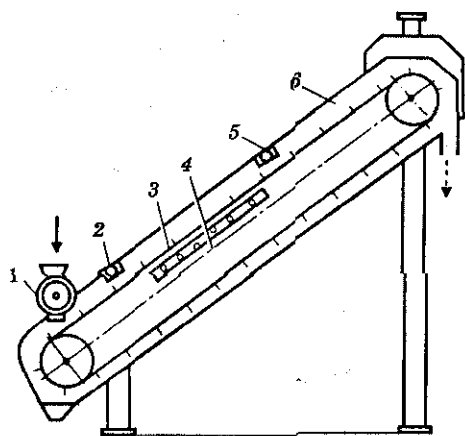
Схема стрічкового розварювача типу БКП:
